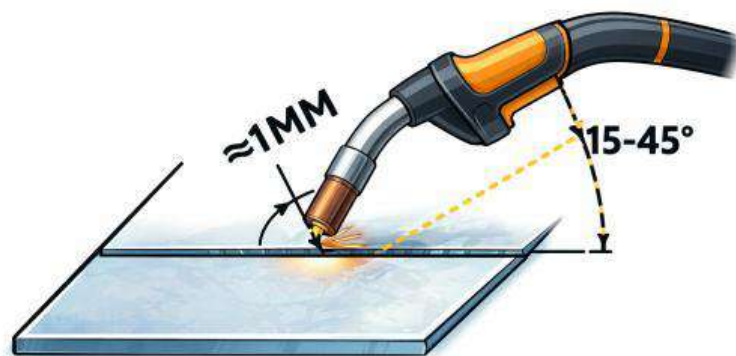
Положення сопла пальника відносно зварного шва
